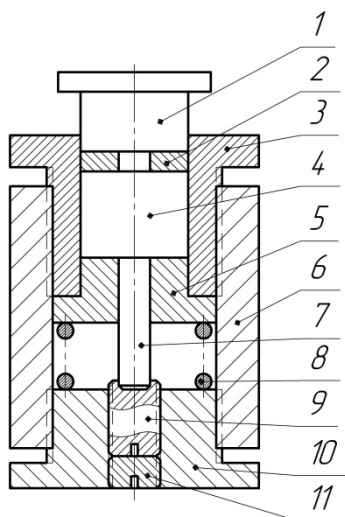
Схема лабораторной установки для сборки заготовок пластическим деформированием: 1 – пуансон; 2 – компенсационная плита; 3 – матрица; 4 – головная заготовка; 5 – упорная вставка; 6 – обойма; 7 – стержневая заготовка; 8 – упругий элемент; 9 – регулировочный винт; 10 – основание установки; 11 – контргайка
